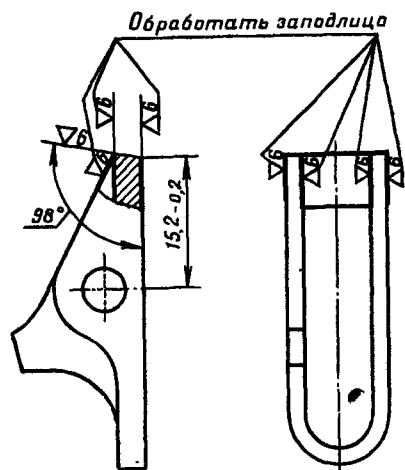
Обработка верхнего торца защелки магазина после наплавки
